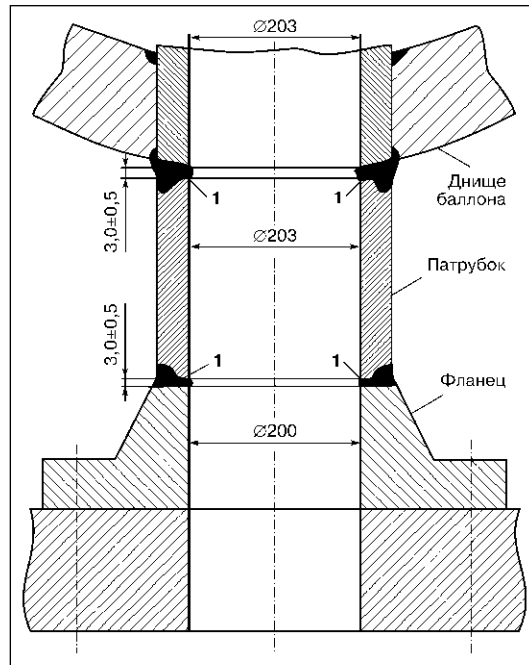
Сварные соединения нового патрубка с днищем и фланцем: 1 — ремонтные сварные соединения и швы
